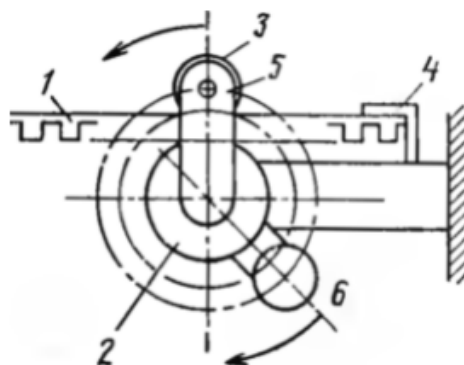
Пристрій для згортання плоских шихтованих пакетів в циліндричні
